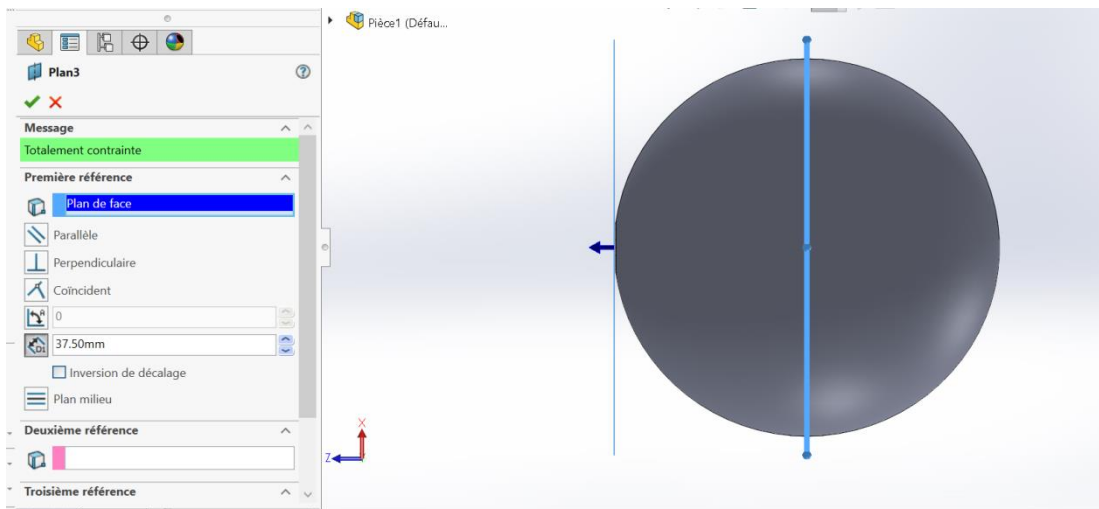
Création d'un nouveau plan parallèle au plan de face
